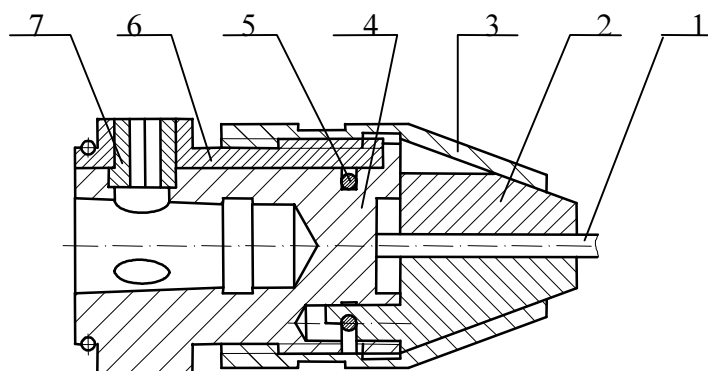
Эксцентриковый сверлильный патрон с ключом
